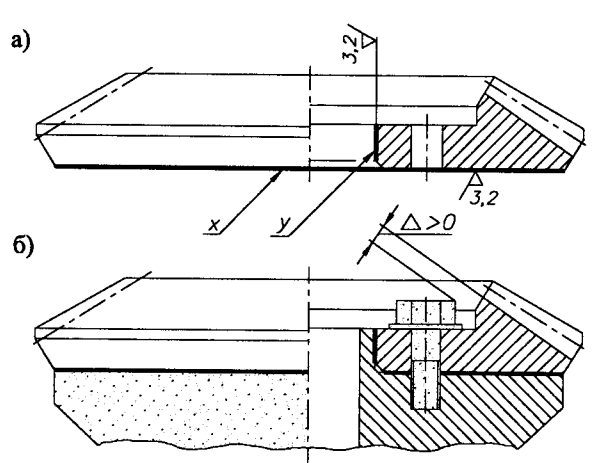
Установочные базы для нарезания зубьев на колесах-дисках
